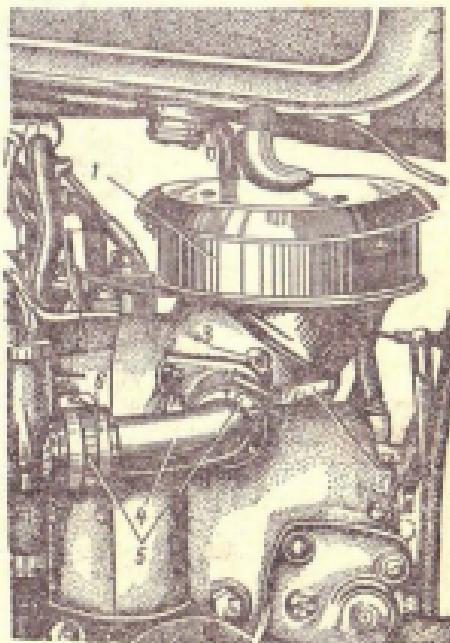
Воздухоочиститель, установленный на корпусе коробки передач:
